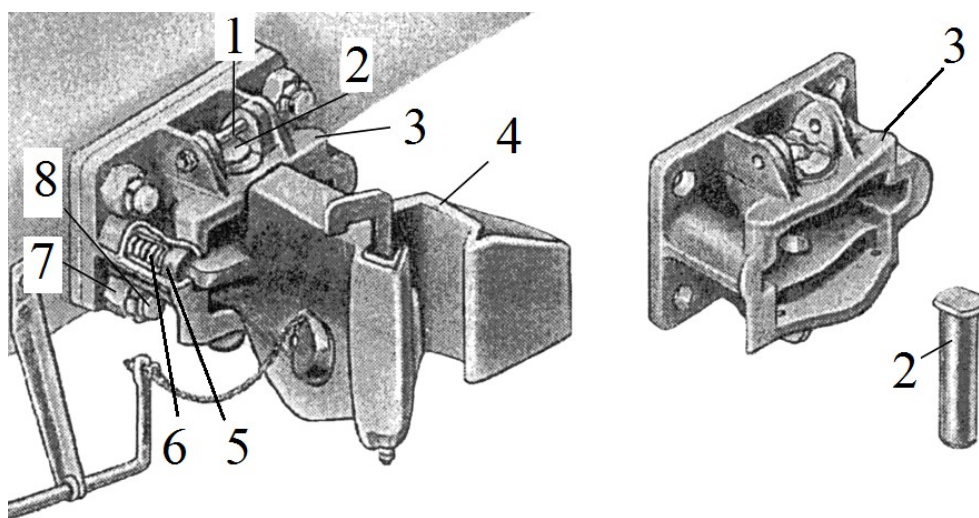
Автозчіпний пристрій без поглинального апарата:
